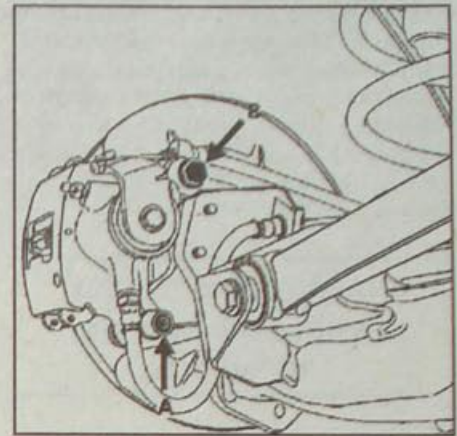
Расположение нижнего (А) и верхнего (В) болтов крепления направляющих пальцев скобы суппорта заднего дискового тормоза
